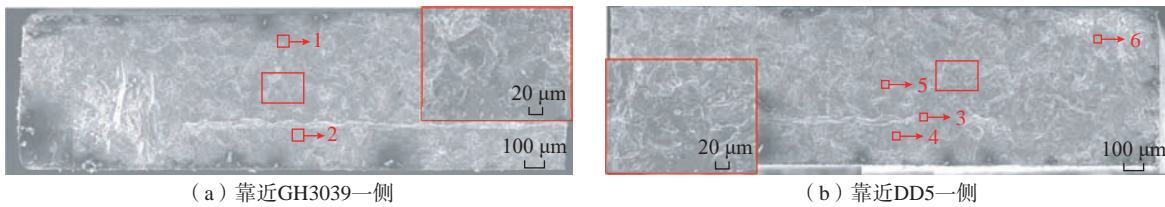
DD5/GH3039 高温合金钎焊接头的拉伸试样断口宏观和微观形貌
